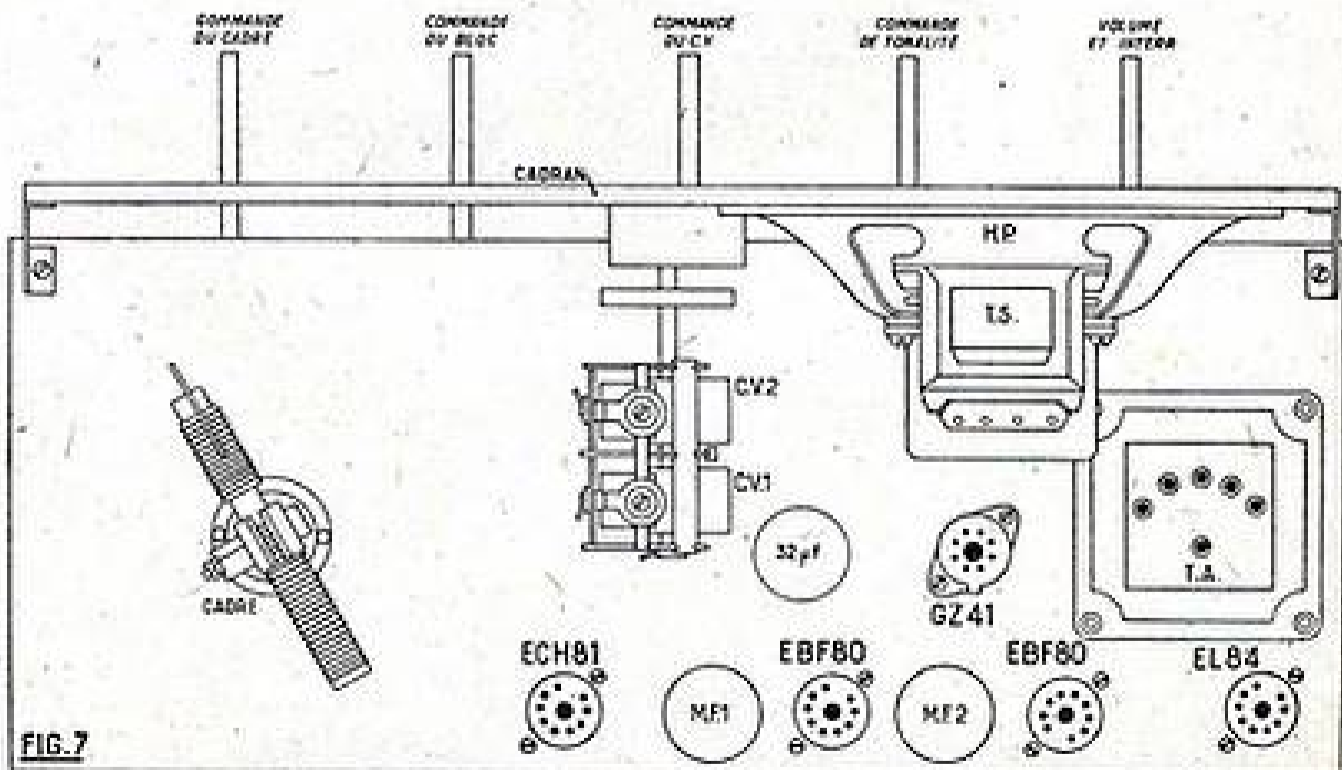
Disposition type dans un récepteur à cadre incorporé.
